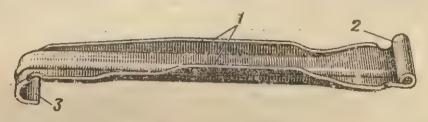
Толкатель щитка: 1 — ребра со скосами; 2 — петля; 3 — загиб
